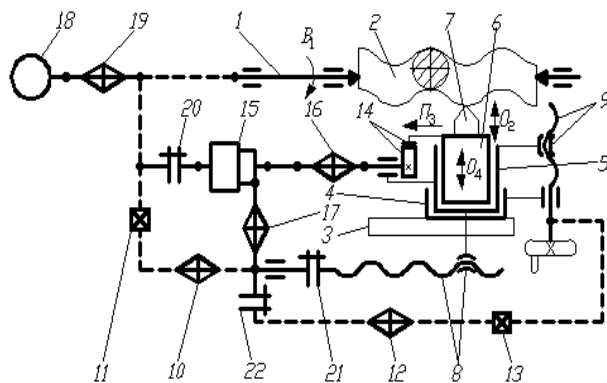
Структурная схема станка для обработки круговых винтовых поверхностей
